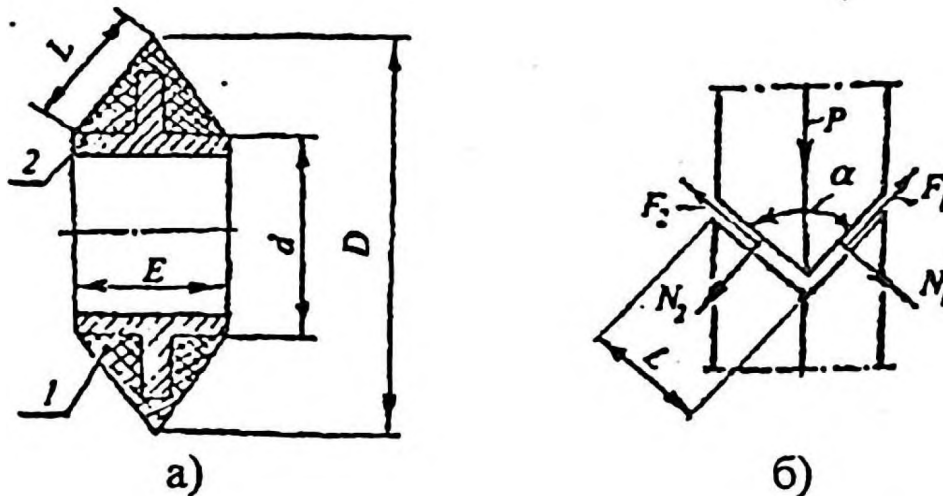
Клиновидный элемент а и схема действия сил б на его рабочей грани L : 1 – резина; 2 – металлическая втулка
